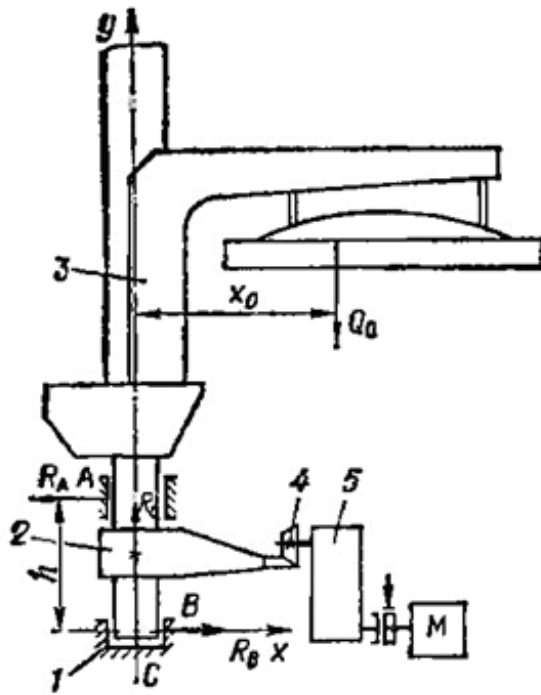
Розрахунково-кінематична схема механізму повороту склепіння
